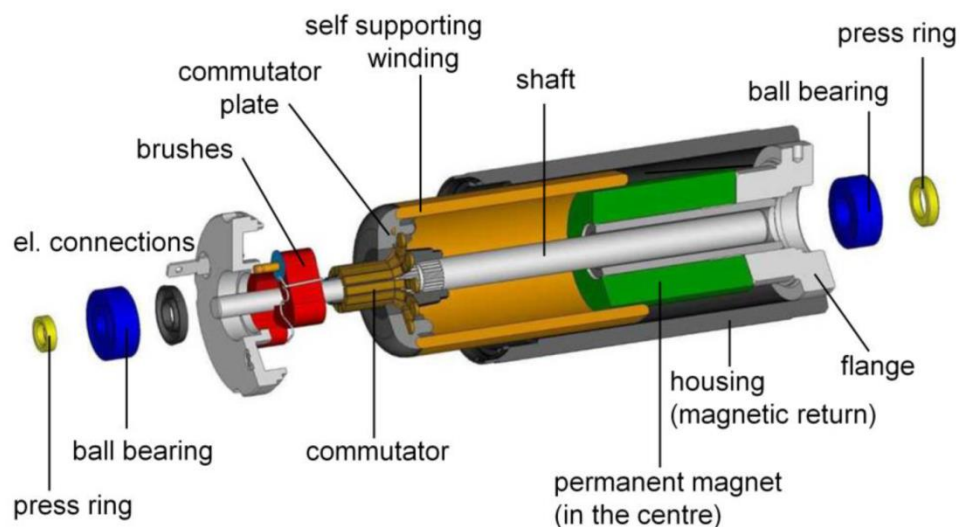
Componentes principales del motor SKU 316030060 [26]
